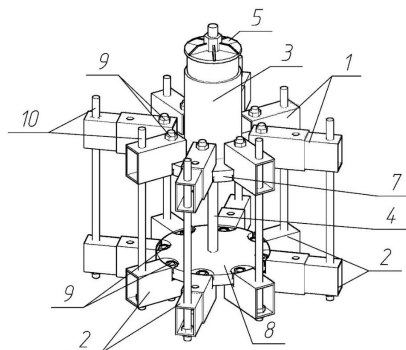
Полезная модель устройства для запрессовки когтевых шайб: 1, 2 – опорные элементы; 3 – механизм для нагнетания нагрузки; 4 – центральный стержень; 5, 6 – гайка-крышка; 7, 8 – втулка; 9 – стяжные элементы; 10 – цилиндрические стержни
